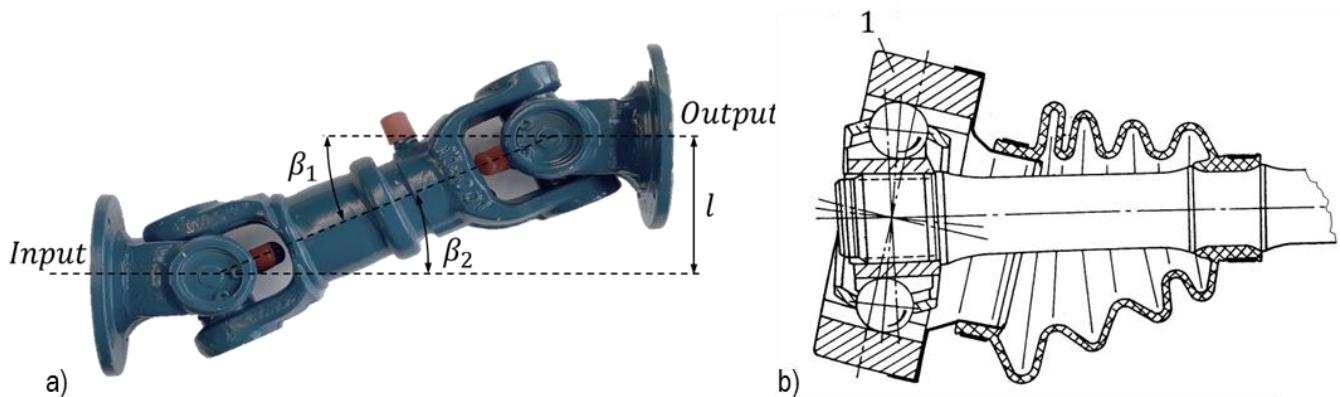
a) Kreuzgelenkwellen / Universal joint driveshaft b) Kugelverschiebegelenk / Ball-Plunging Joint
